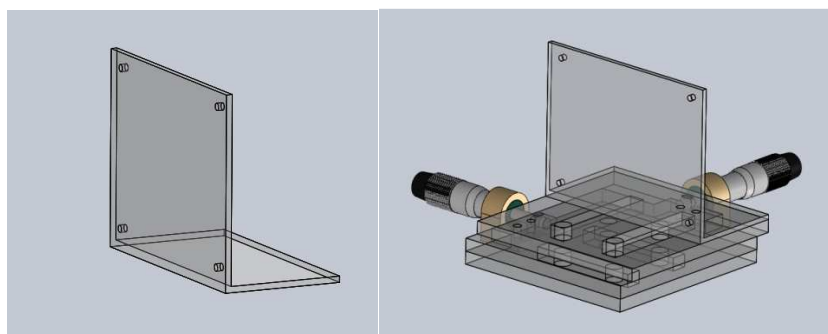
a) Diseño 3D del soporte para rotativo b) Diseño 3D del conjunto X-Y
